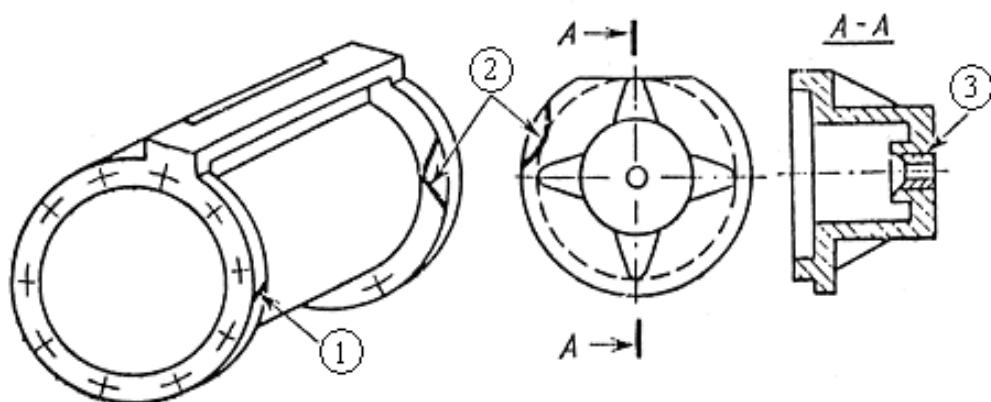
Дефекты тормозного цилиндра марки 501Б, ремонтируемые сваркой
